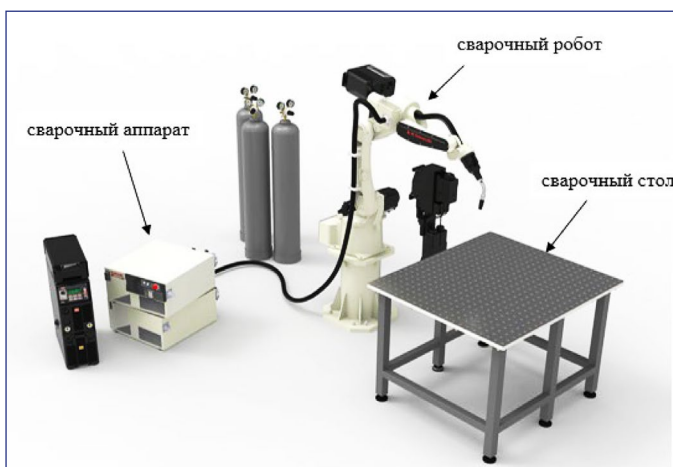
Базовое решение для роботизированного сварочного комплекса
